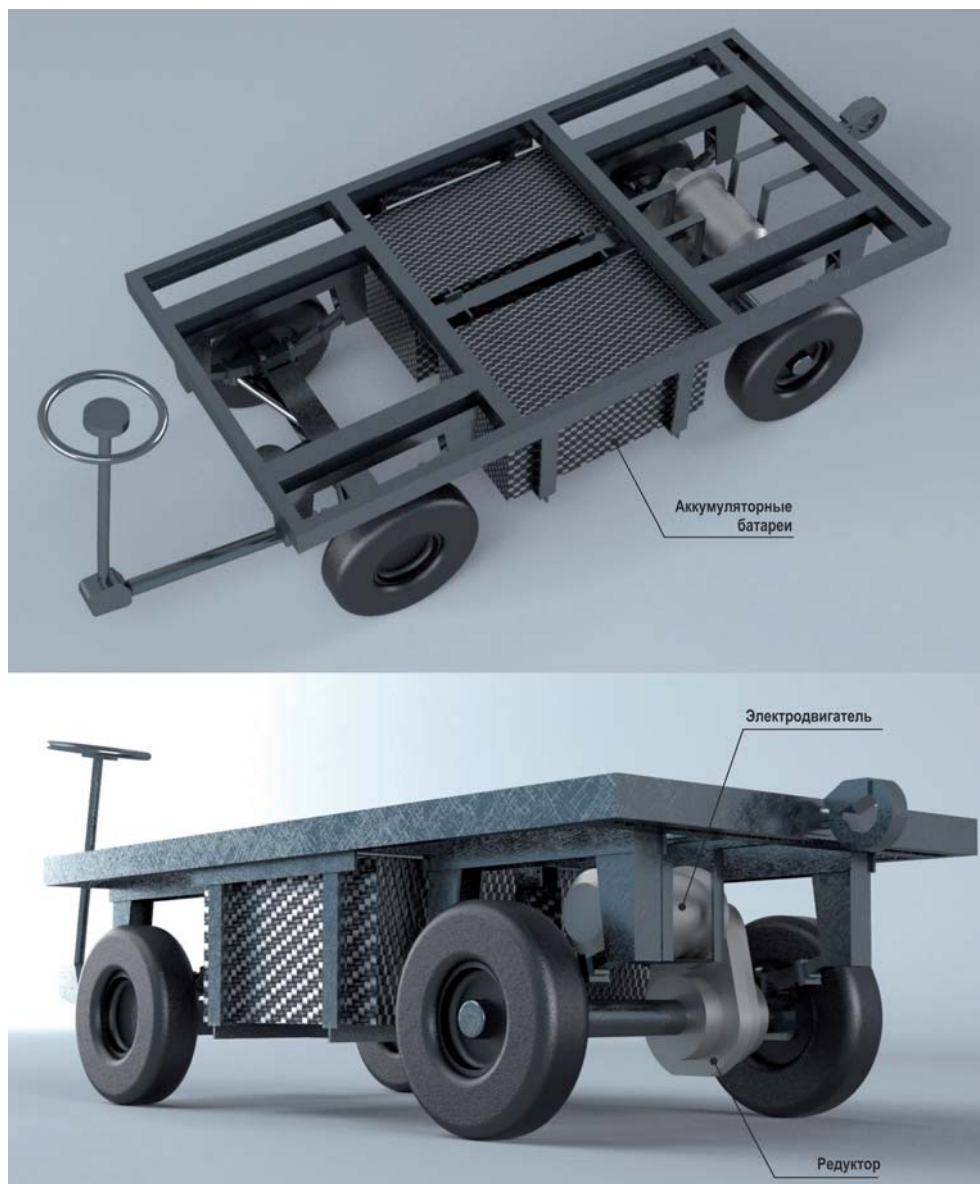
Общая конструкция рамы с узлами и агрегатами
